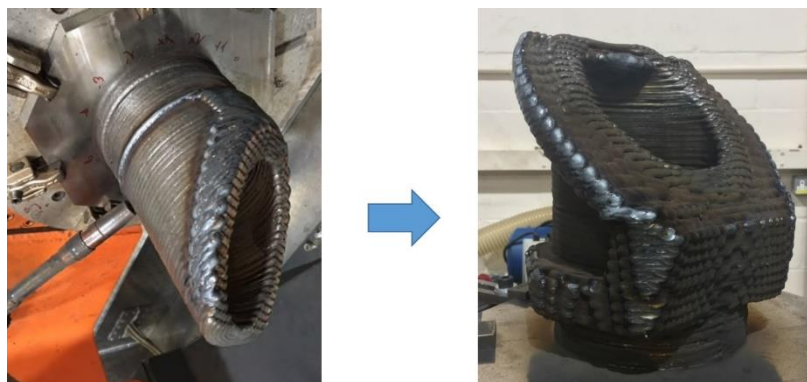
Fertigung einer Rohrleitungskomponente mit dem WAAM – Verfahren (Martina, 2023)
